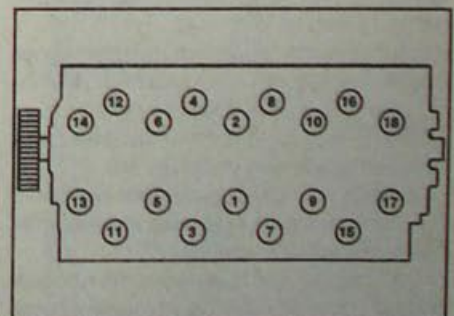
Нумерация болтов крепления головки цилиндров двигателя G8T
